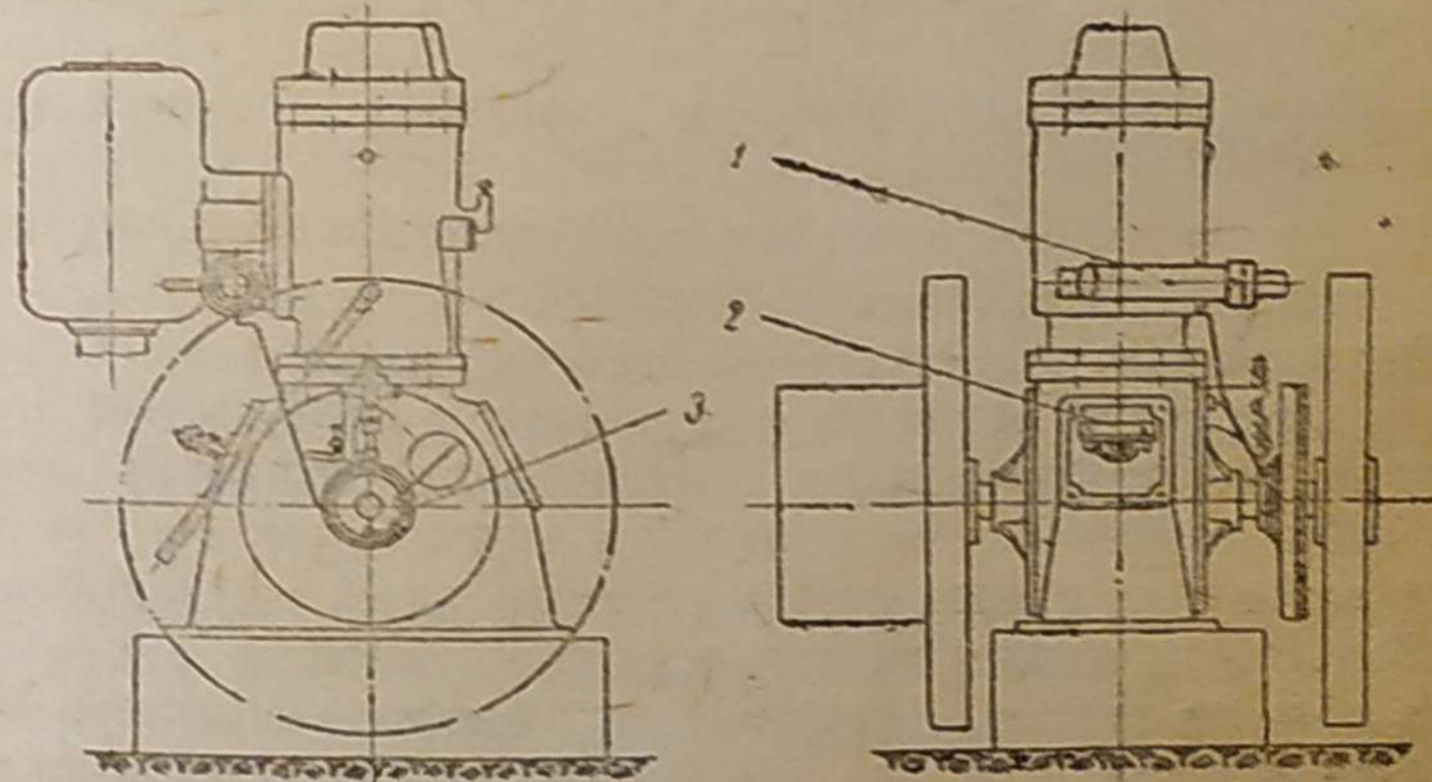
Двухтактный нефтяной двигатель, переоборудованный для работы на газе:
